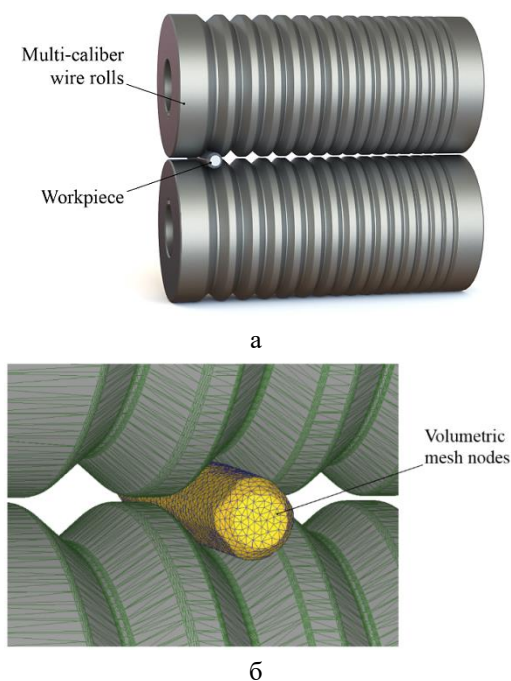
Общий вид модели сортовой прокатки прутков: а – модель валков в SolidWorks; б – модель процесса прокатки заготовки с конечно-элементной сеткой в Deform-3D
